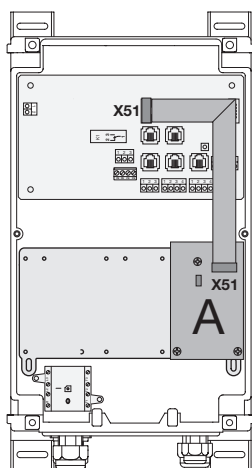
Balíček příslušenství rozšiřovací deska
